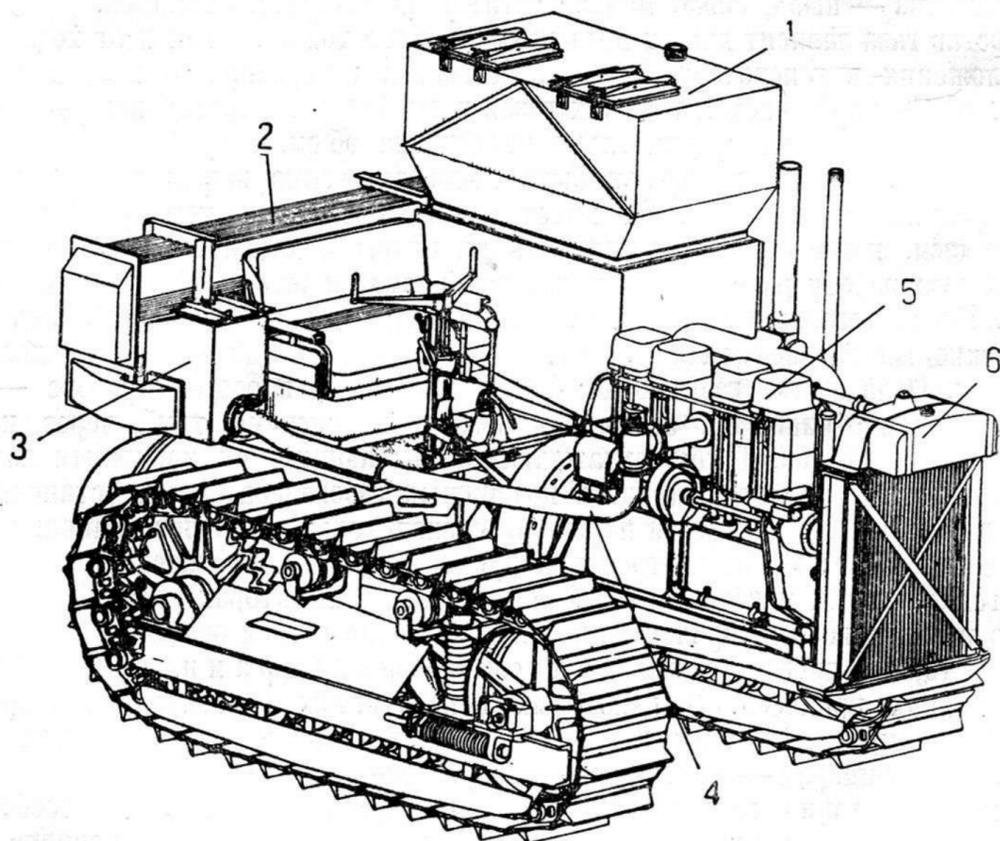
Общий вид установки ОКБ-8 на тракторе „Сталинец“ ЧТЗ. 1—газогенератор; 2—охладитель газа; 3—очиститель газа; 4—газопровод; 5—двигатель; 6—пу-
